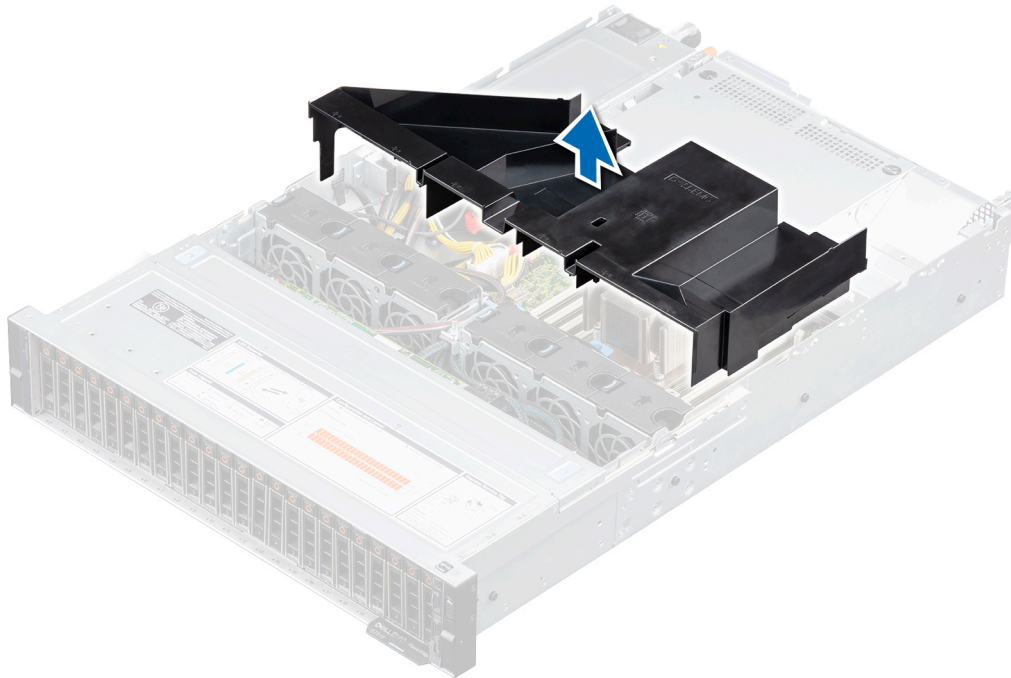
Entfernen des Kühlgehäuses für ein System mit rückseitigen Laufwerken
